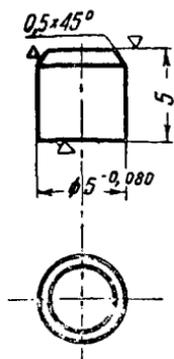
Дет. № 311. Заглушка отверстия корпуса дросселя
